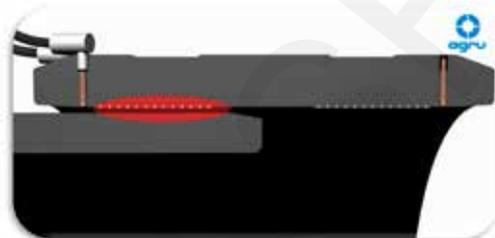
Принцип сварки с двумя нагревательными спиральями.
